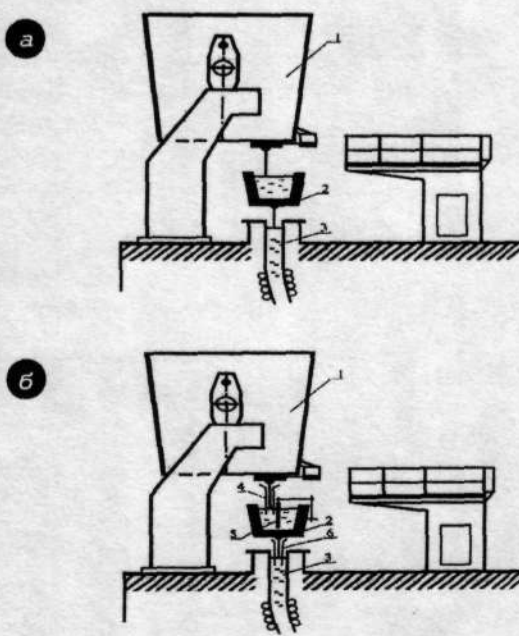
Схема разлива стали на сортовые заготовки открытой струей а) и с защитой стали от вторичного окисления б): 1 – сталеразливочный ковш; 2 – промежуточный ковш; 3 – кристаллизатор; 4 – защитная труба; 5 – стопор; 6 – погружной стакан
